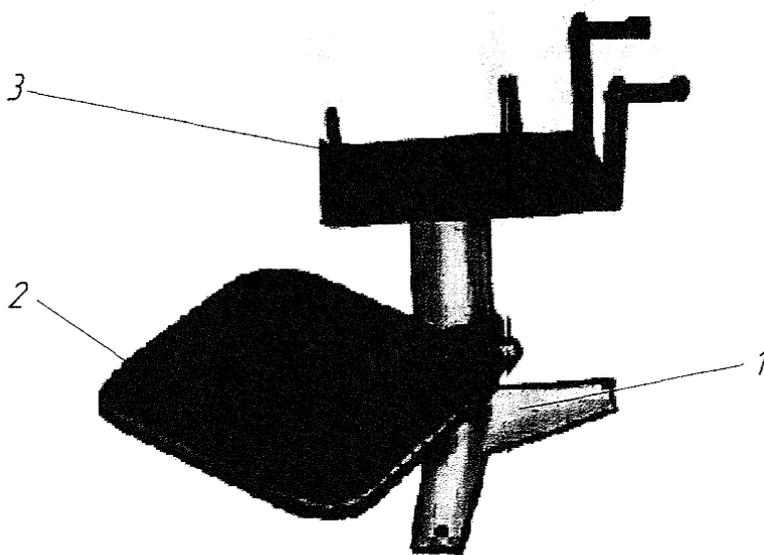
Стенд универсальный для разборки сборки коробок передач
